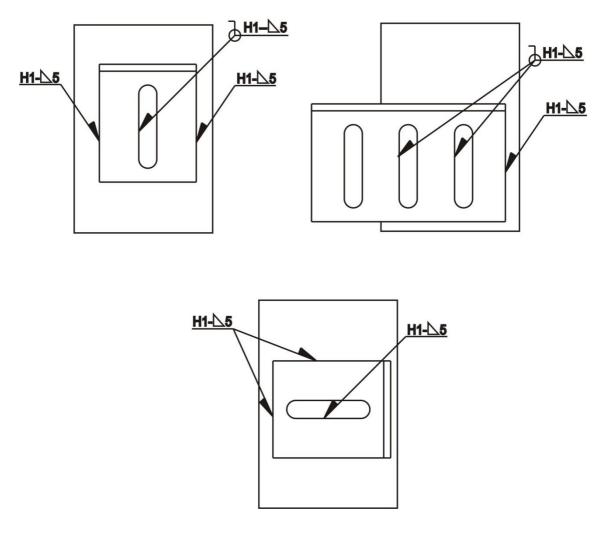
Расположение сварных швов на уголках
